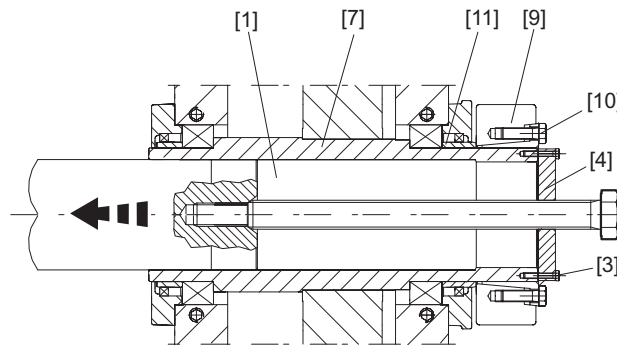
Смонтированный горизонтальный редуктор со стяжной муфтой
